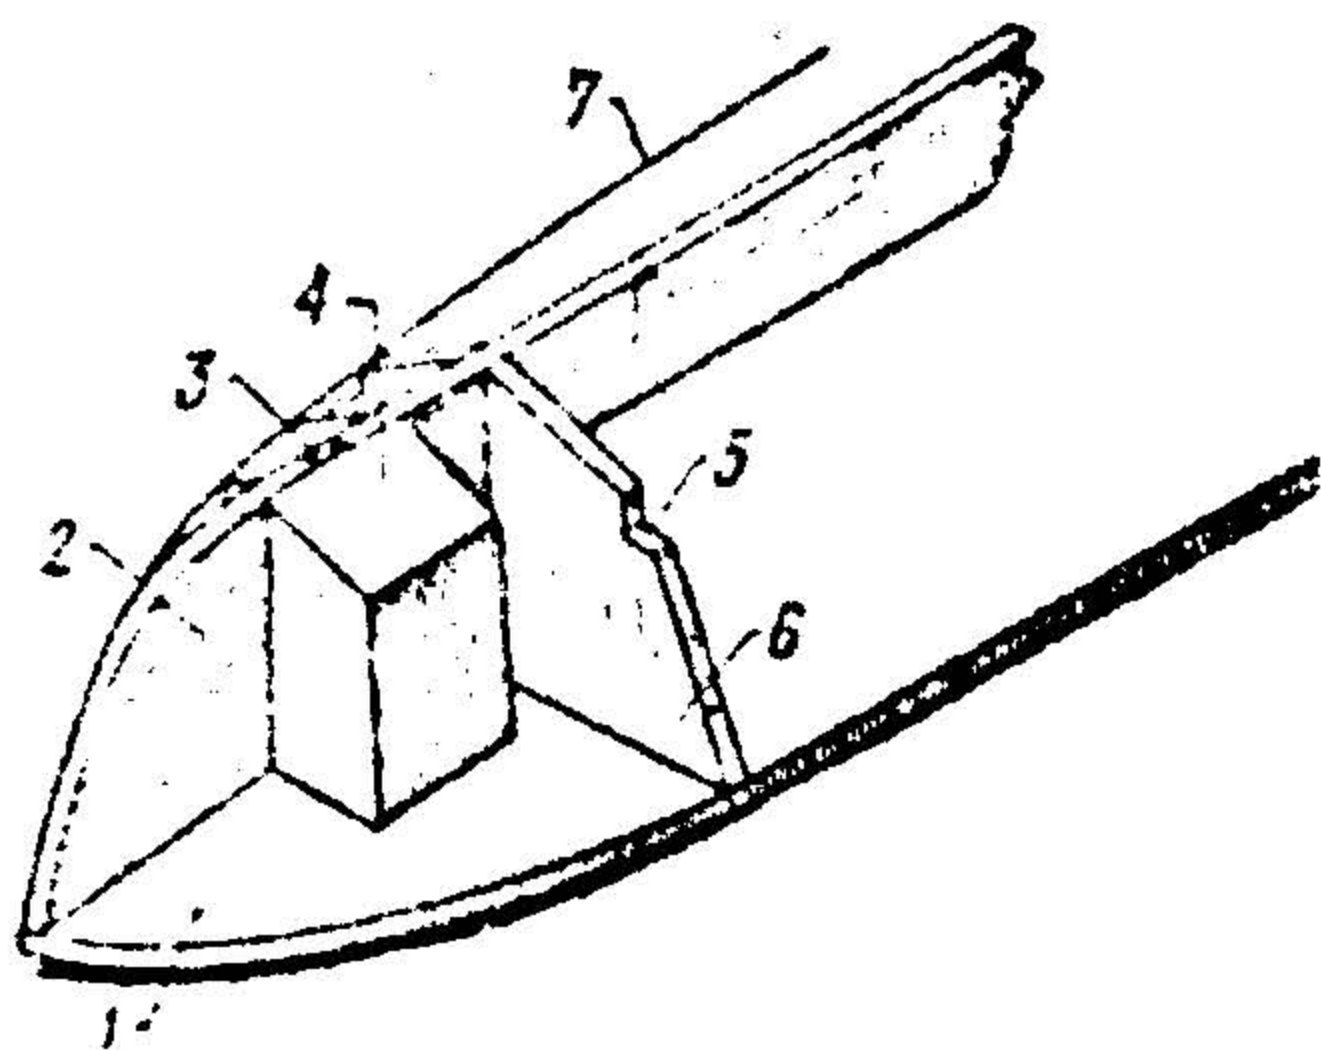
Носовая часть набора: 1 — настил палубы; 2 — килевая рамка; 3 — отверстие для носового крючка; 4 — бруски; 5 — вырез для стрингера; 6 — глухой шпангоут; 7 — стрингер
